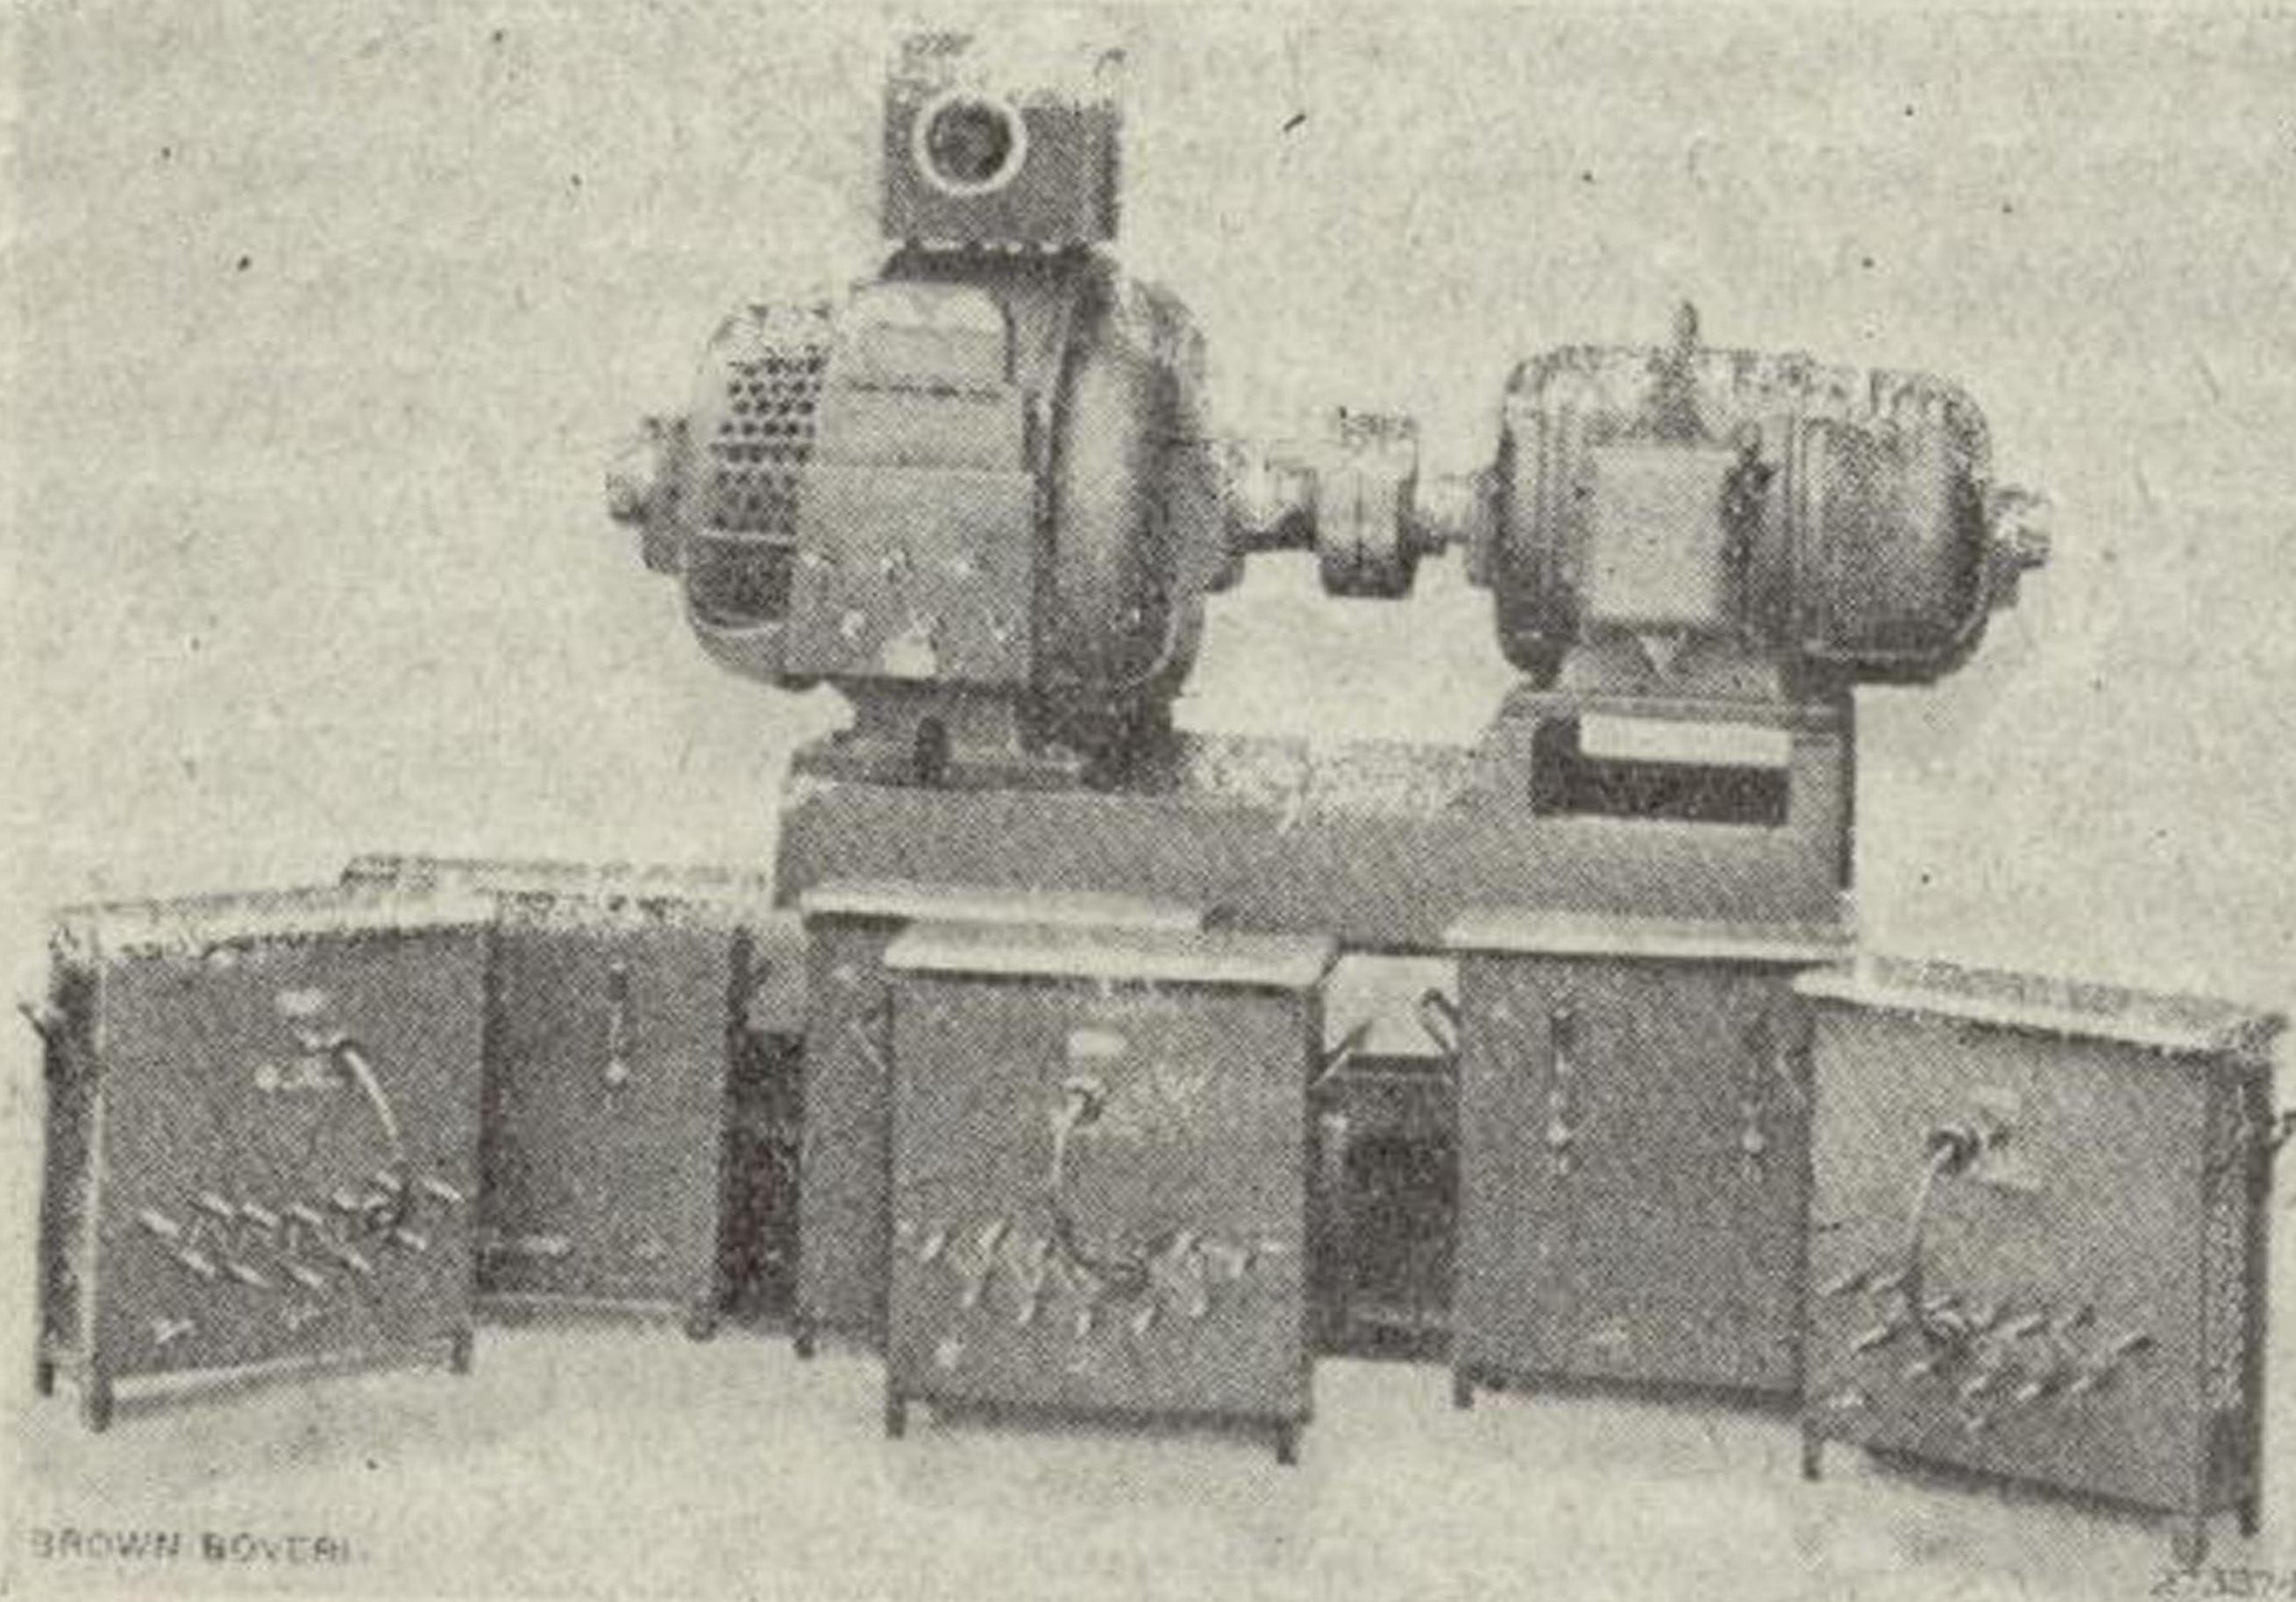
^a.—Grupo de soldadura por arco para la alimentación de tres electrodos de 180 amperios cada uno con tres grupos de reguladores de la corriente de soldadura.
